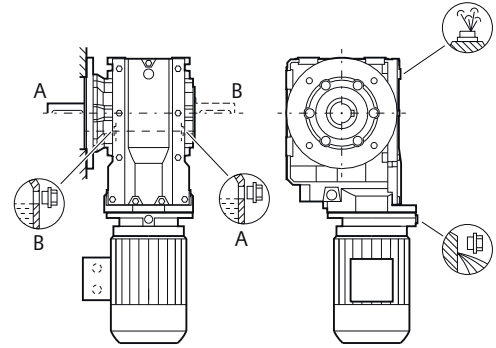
Konik dişli için montaj konumları B.F Flanşlı model ve gövde flanşlı B.Z, Boyut 19 - 29
